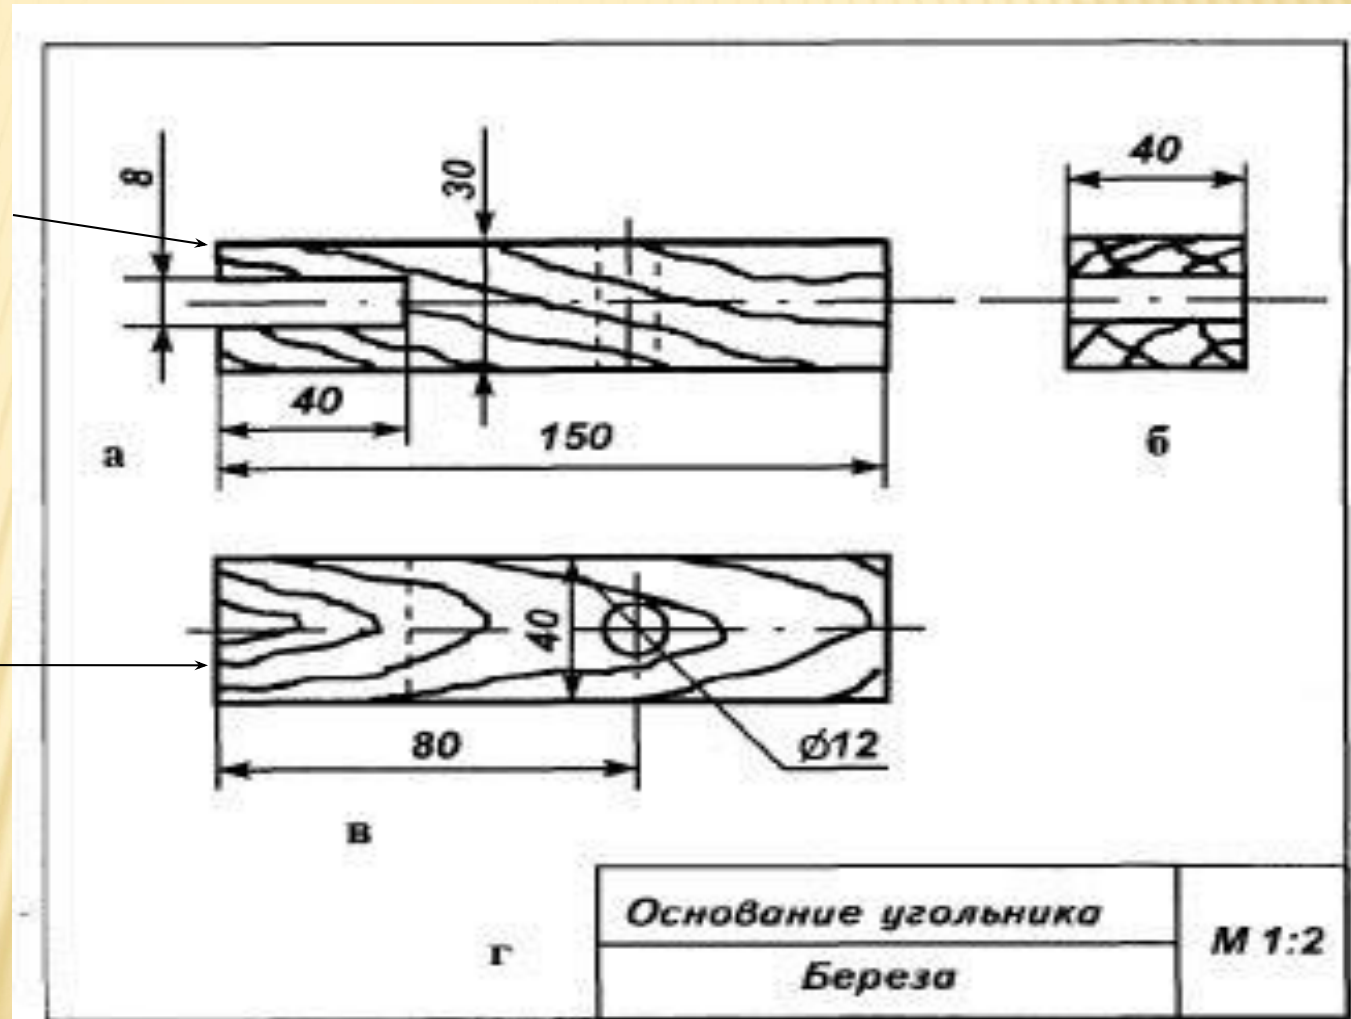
Чертеж призматической детали: а — главный вид; б — вид слева; в — вид сверху; г — основная надпись
